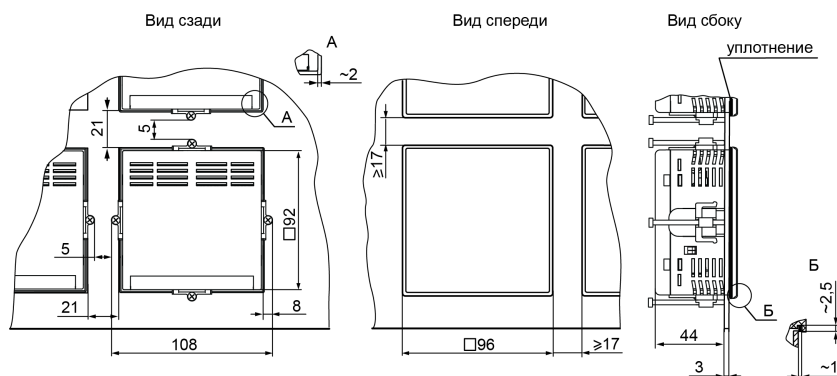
Прибор в корпусе Щ1, установленный в щит толщиной 3 мм
